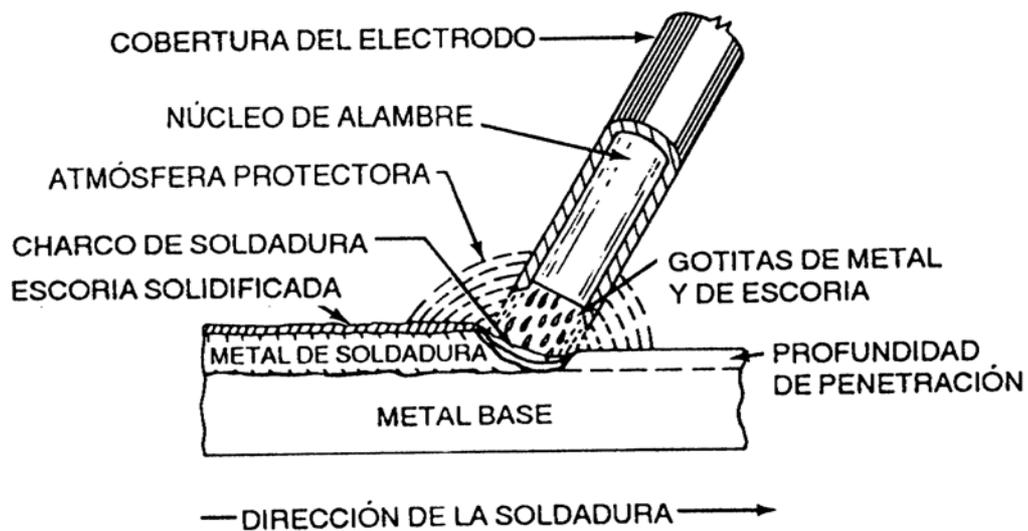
Acción protectora del arco en la soldadura por arco de metal protegido
